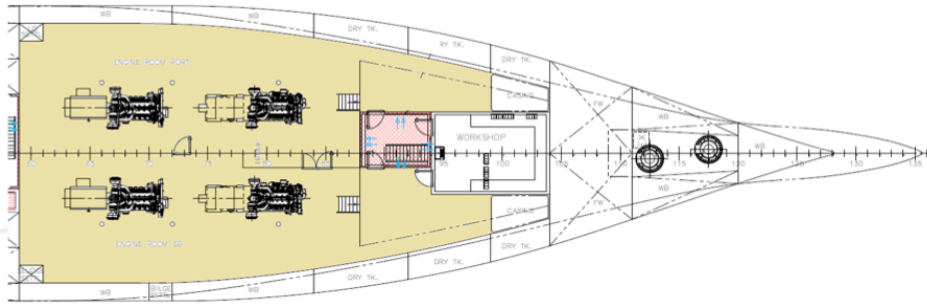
Aislamiento del techo de la sala de máquinas: techo.
